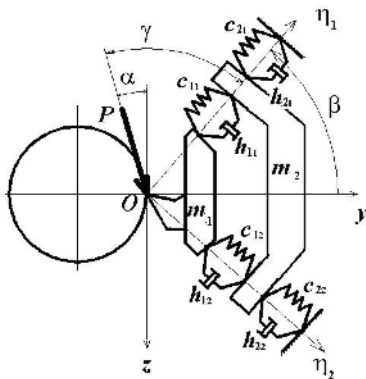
Розрахункова схема пружної системи різець-супорт токарного верстата в площині yOz
